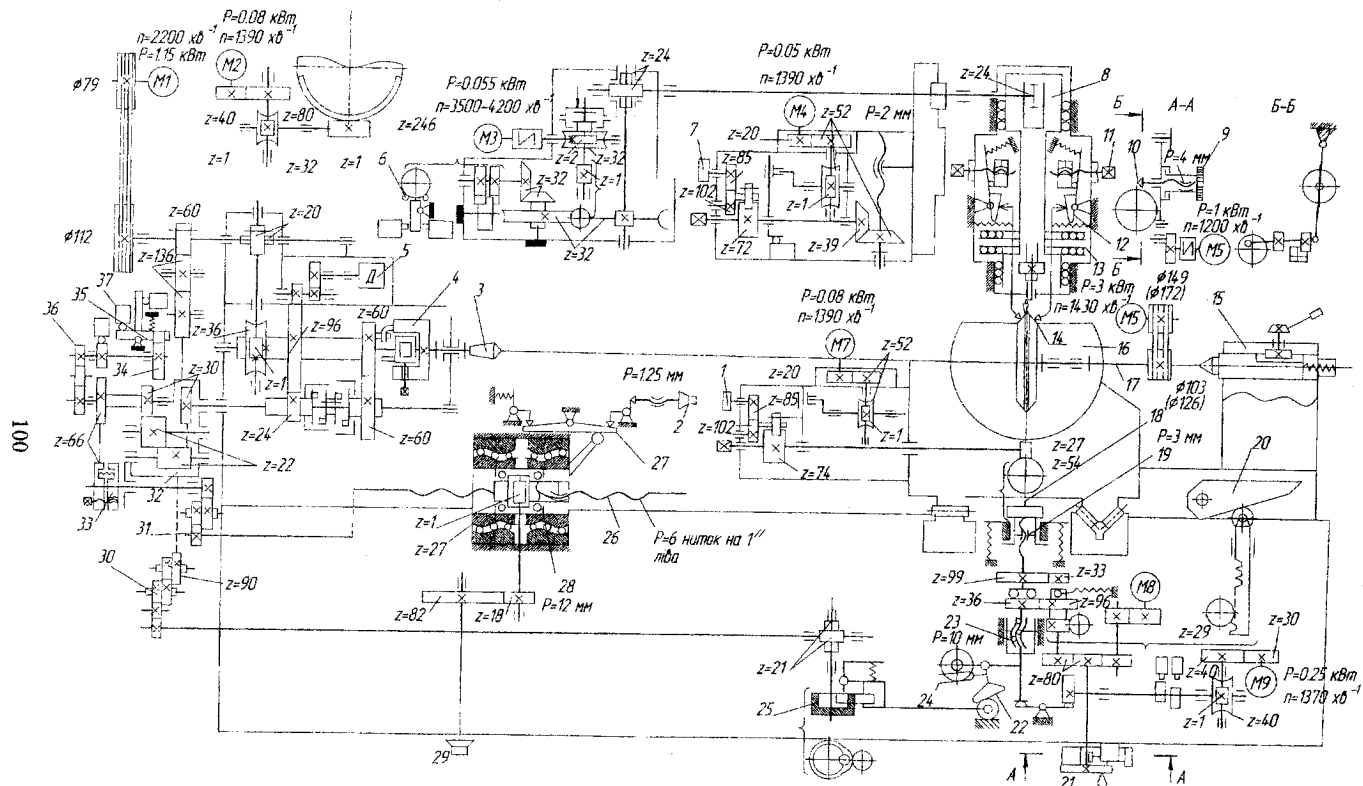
Кінематична схема універсального різьбошліфувального верстата без ЧПК 5K822
